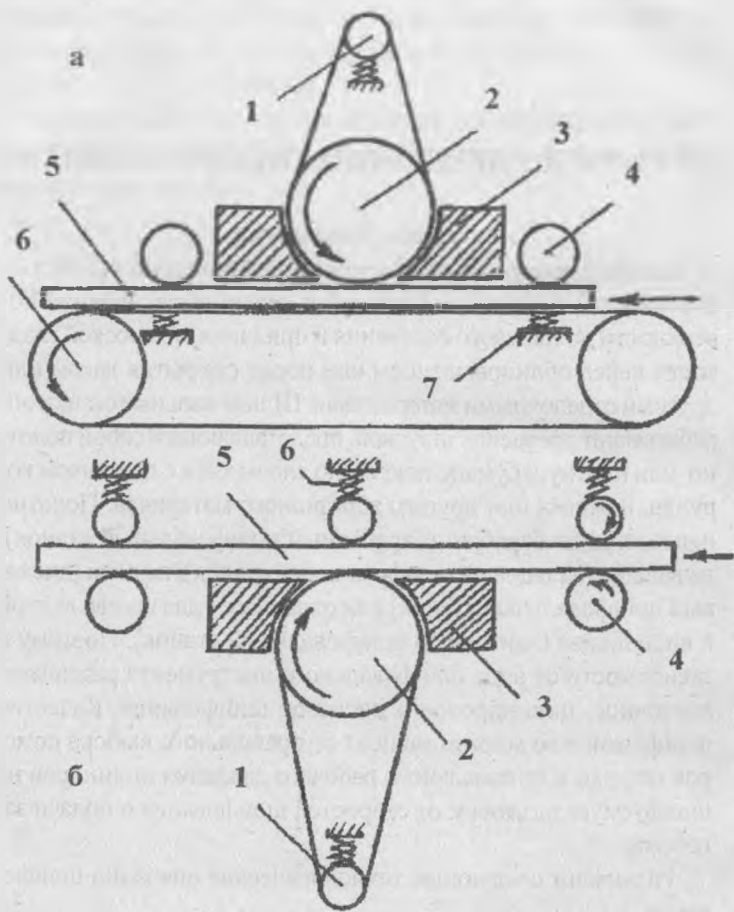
Наиболее типовые схемы широколенточных станков для выравнивания и чистовой обработки:
